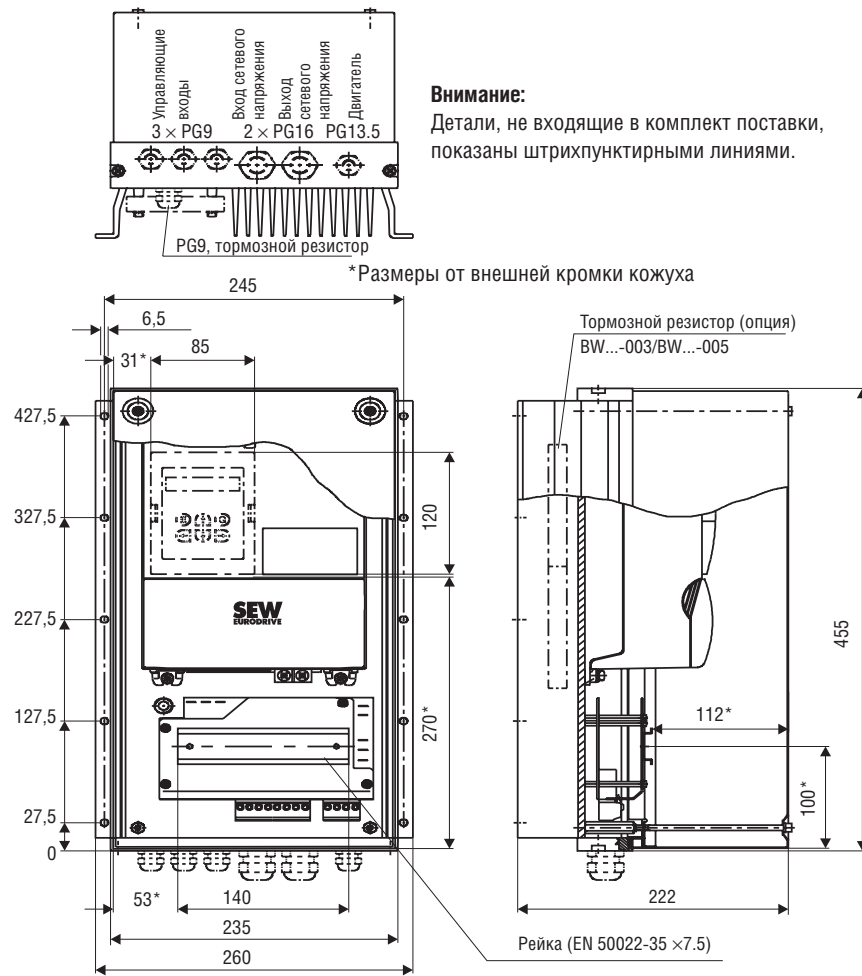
Габаритный чертеж преобразователя частоты для децентрализованного монтажа
